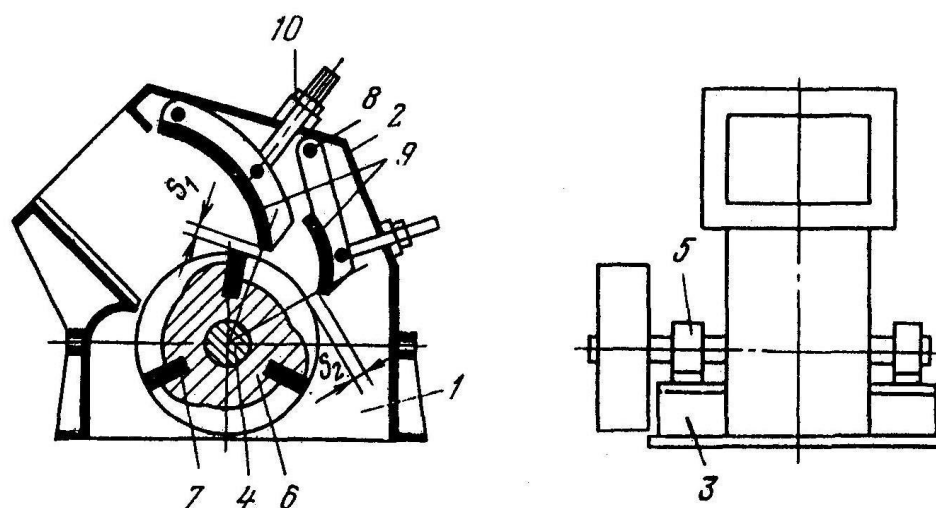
Однороторна дробарка крупного дроблення (типу ДРК) [16, 17, 21]
